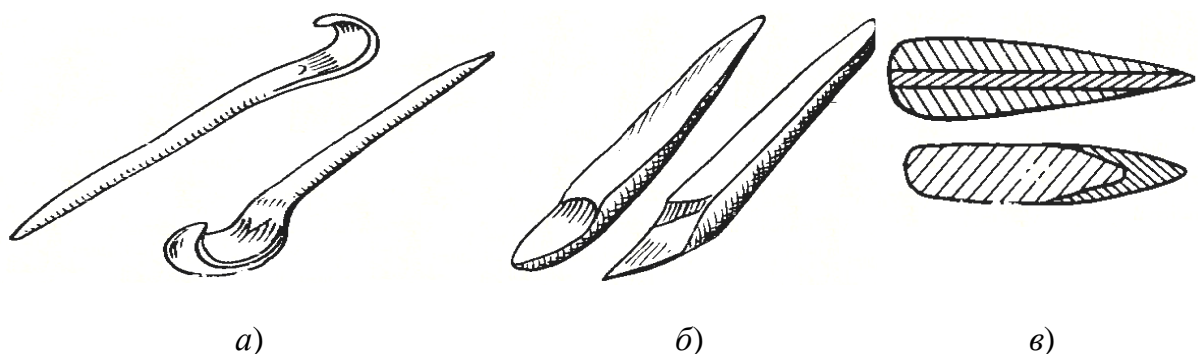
Резцы Древней Руси 9–10 вв.:
